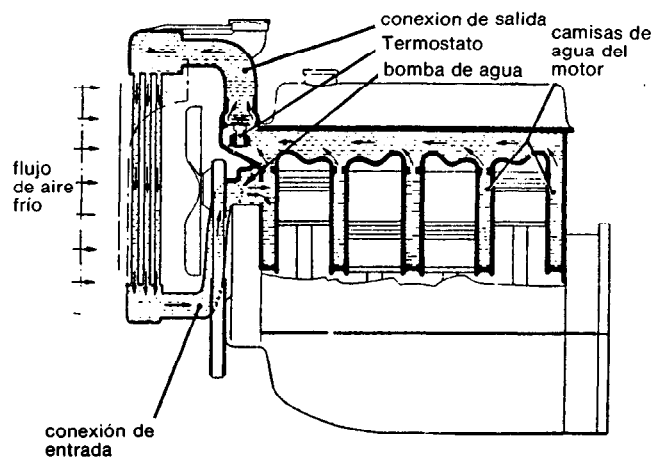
Parte básica de un sistema de enfriamiento FORD
